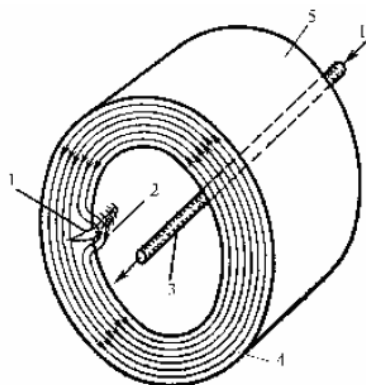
Схема циркулярного намагничивания детали пропусканием тока по стержню: 1 – трещина; 2 – поле рассеяния над трещиной; 3 – стержень; 4 – магнитные линии; 5 – деталь; I – ток
